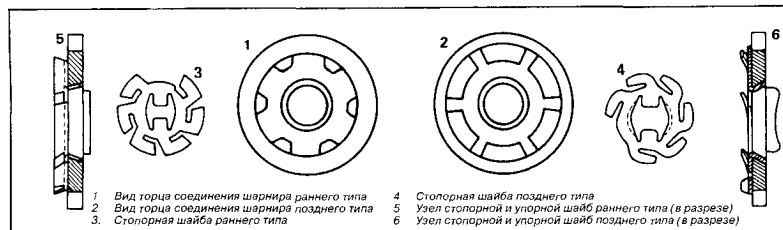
Два типа блокировки соединения рейки и шарнирного наконечника
